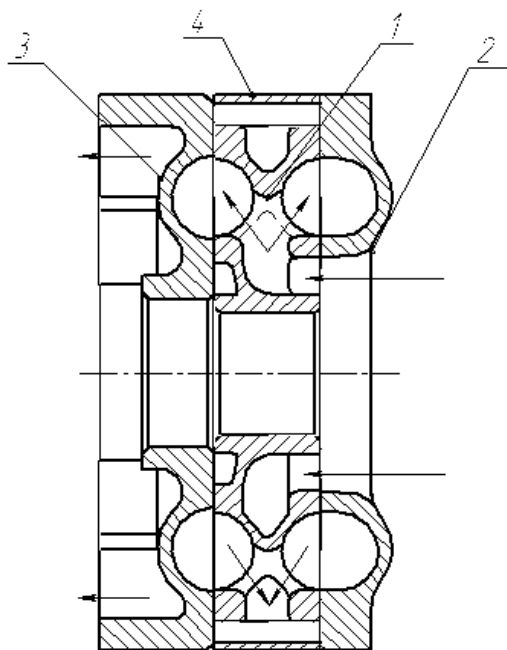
Загальний вид ступені: 1 – робоче колесо; 2 – передня вихрова ступень; 3 – задня вихрова ступень; 4 – корпус робочого колеса
